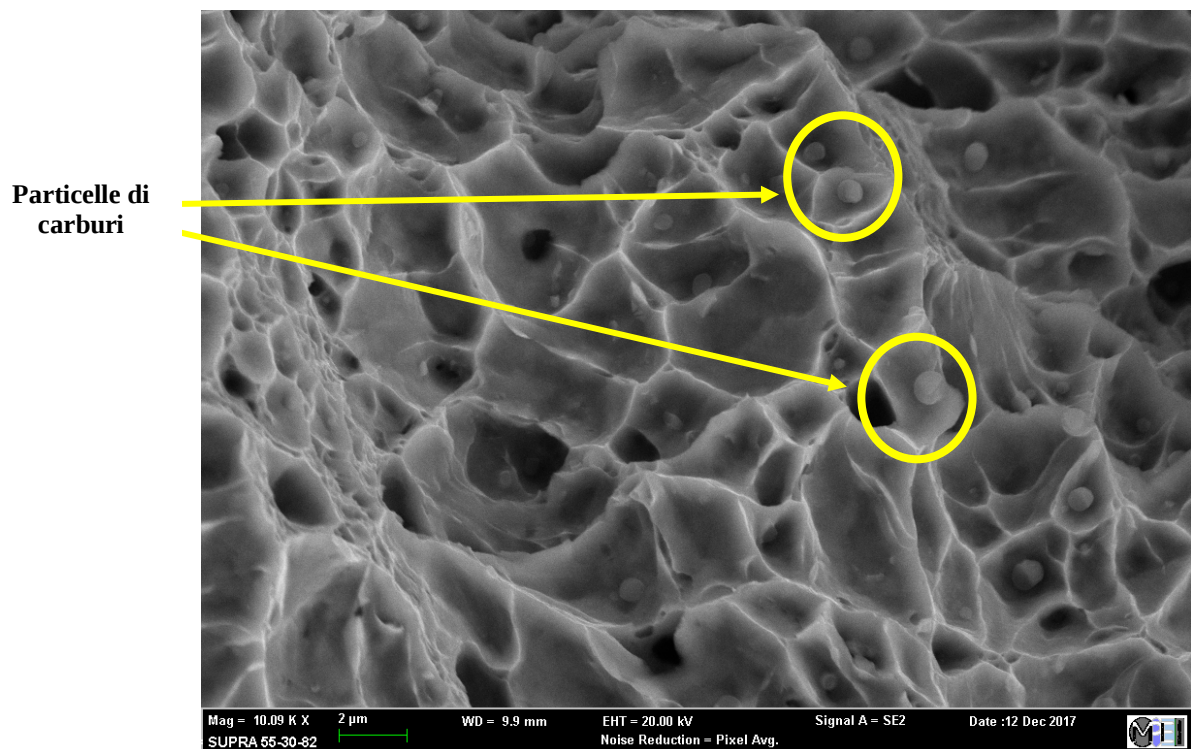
Immagine ad elevato ingrandimento (10000 ×) che mostra in dettaglio i dimples e le particelle di carburi nel materiale trattato a 540° C
